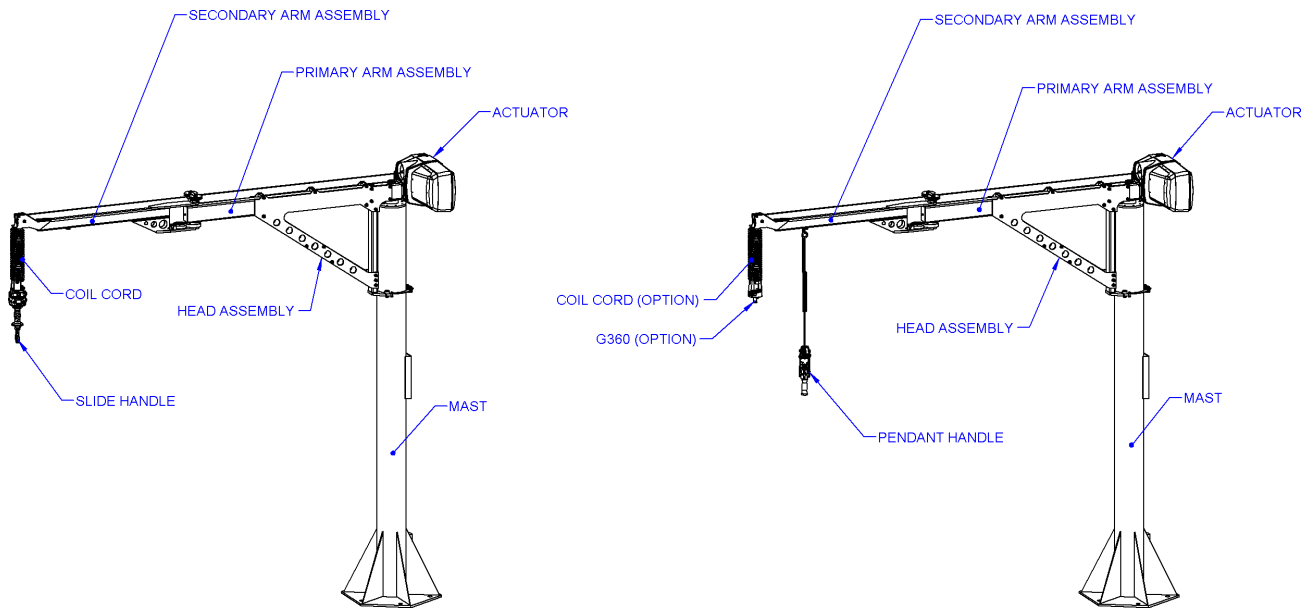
A. Principali componenti di Easy Arm® con montaggio a terra.
